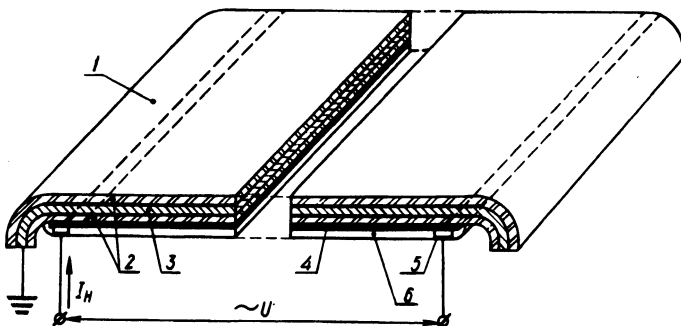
Принципиальная конструктивная схема полупроводникового пленочного электрообогревателя: 1 — рабочая теплоотдающая поверхность; 2 — стеклоэмалевая изоляция; 3 — металлический корпус; 4 — пленочный нагревательный элемент; 5 — контактные токоподводящие электроды; 6 — внешнее термостойкое электроизоляционное покрытие.
